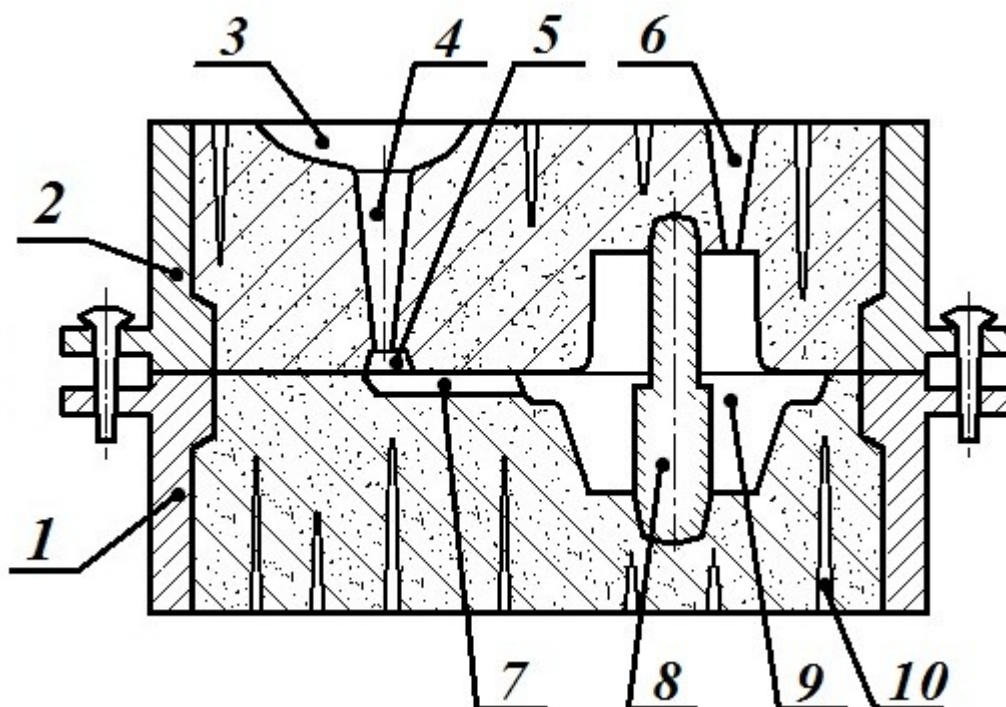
Эскиз разреза песчаной формы для отливки чугунного фланца:
